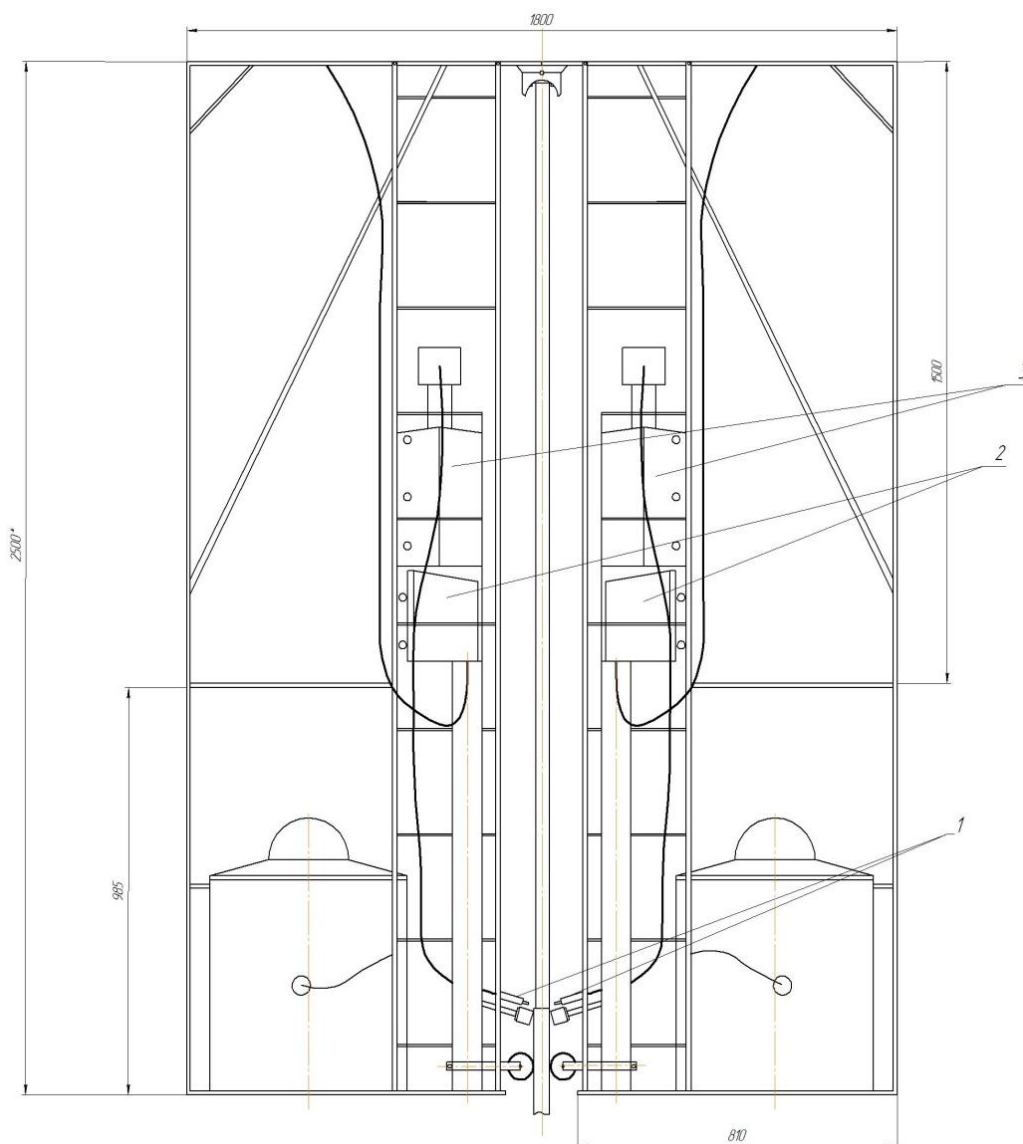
Установка для автоматической сварки под флюсом АГВ-II:
